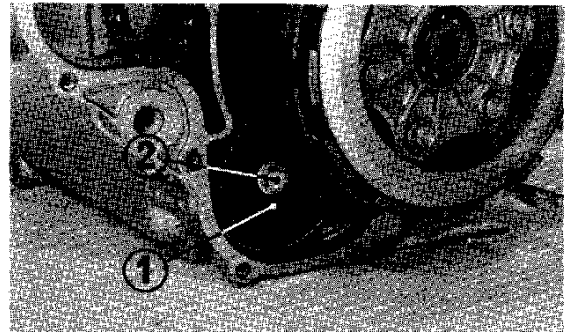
(1) Ölpumpen-Antriebskettenrad
